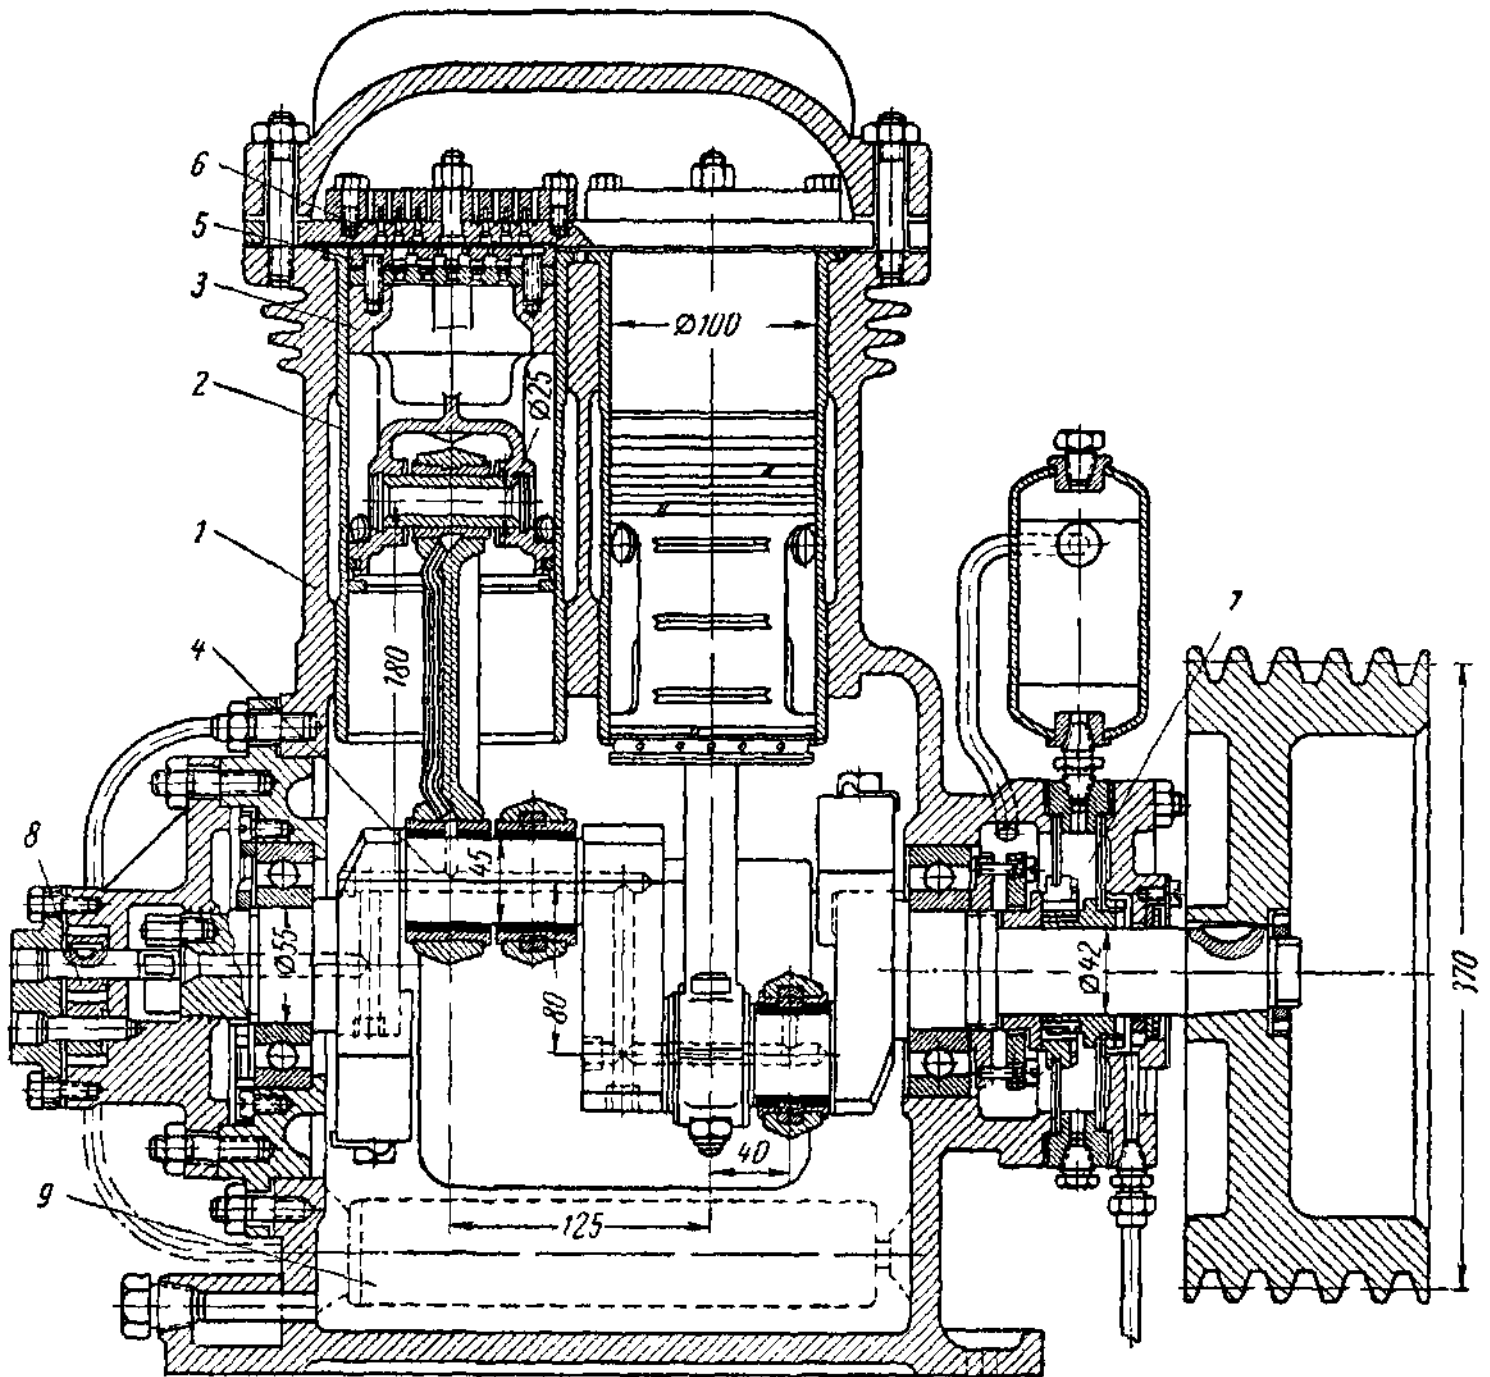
Блоккартерный четырехцилиндровый фреоновый проточный компрессор 4ФУ-10:
